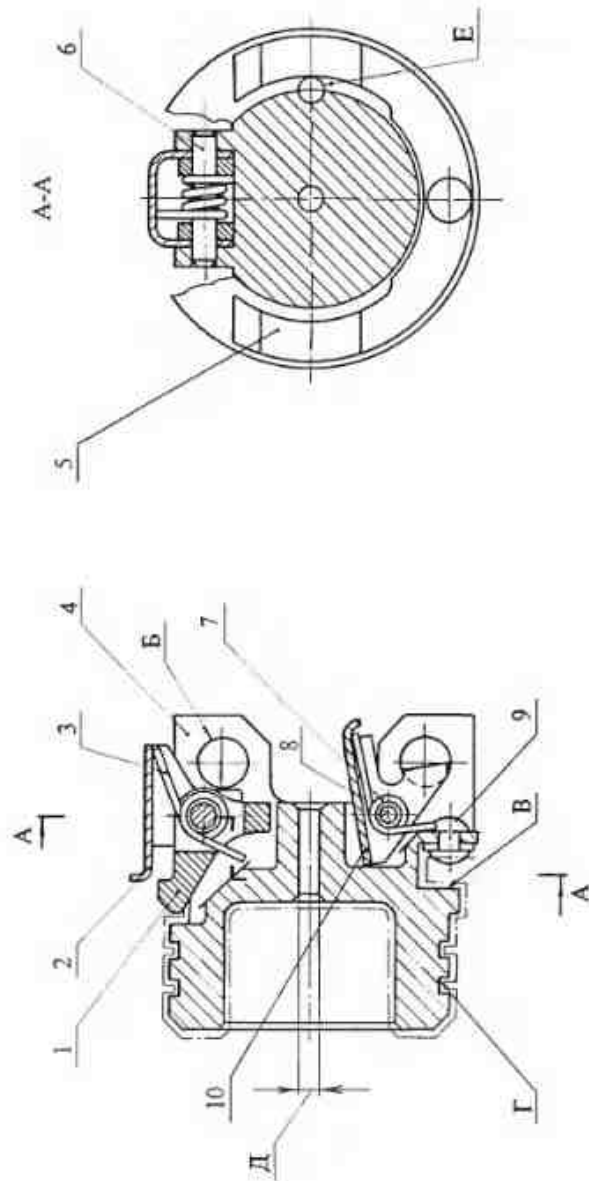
(лист 1 из 2) - Корпус с казенником
